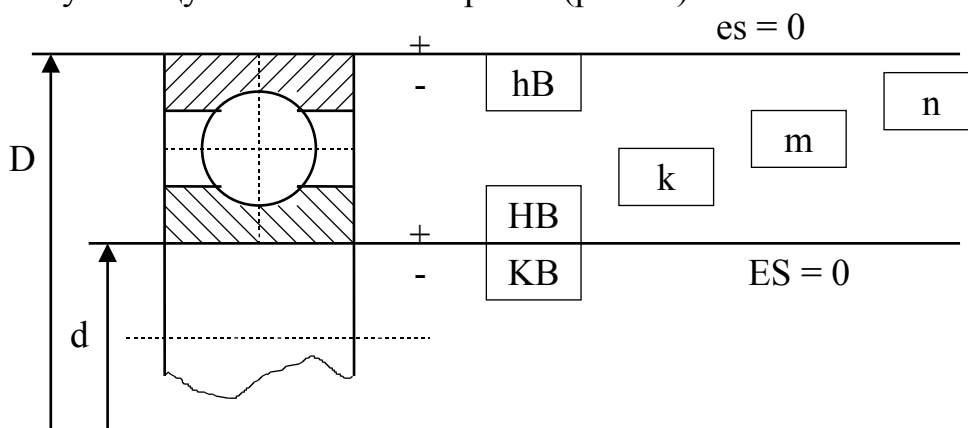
Схема расположения полей допусков по присоединительным размерам
